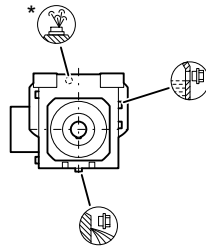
Konstrukcje dla D/Z wielkości 108 - 168
